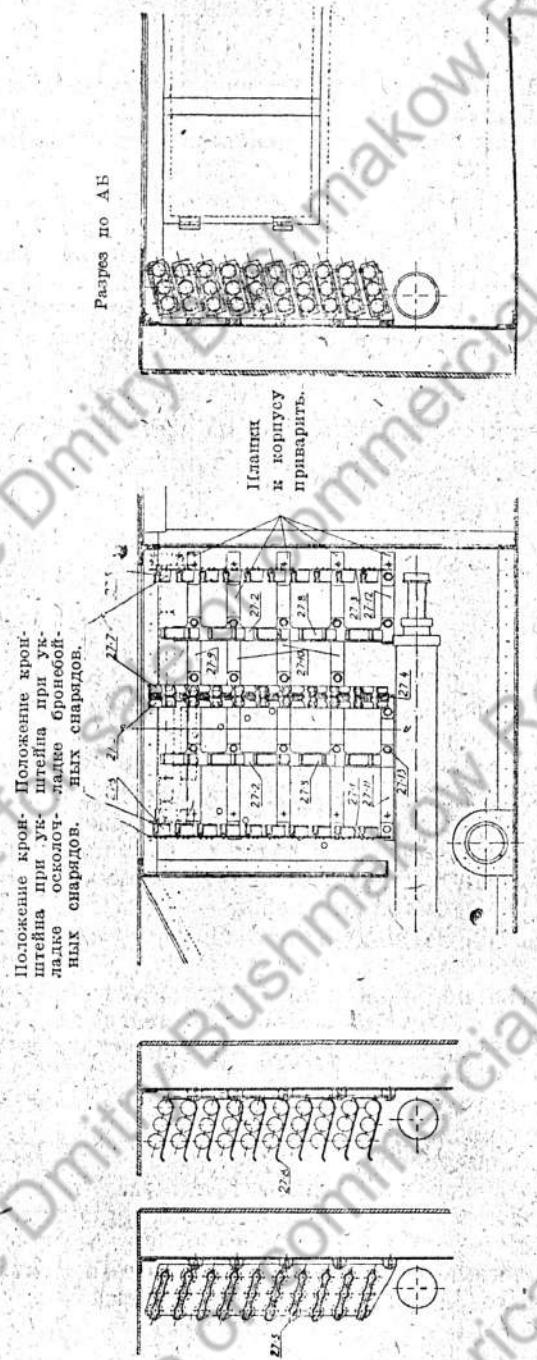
Укладка снарядов на правой боковой стенке корпуса.
